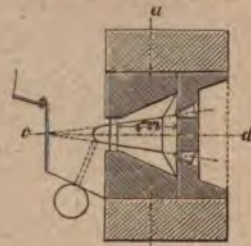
Grundriß nach gh. Doppelschachtofen.
